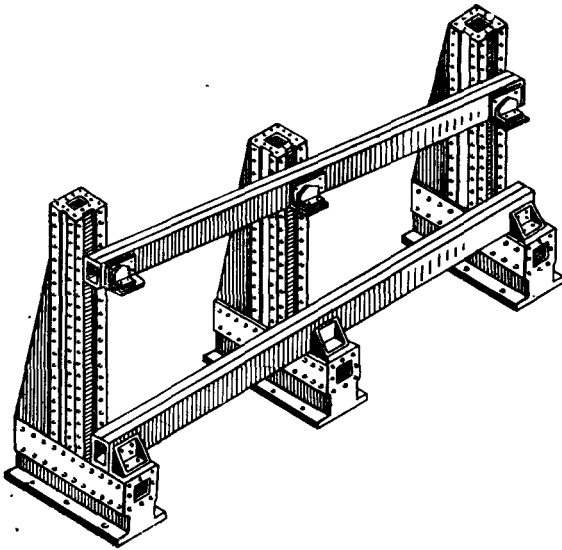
Стандартные элементы трубчатых приспособлений:
